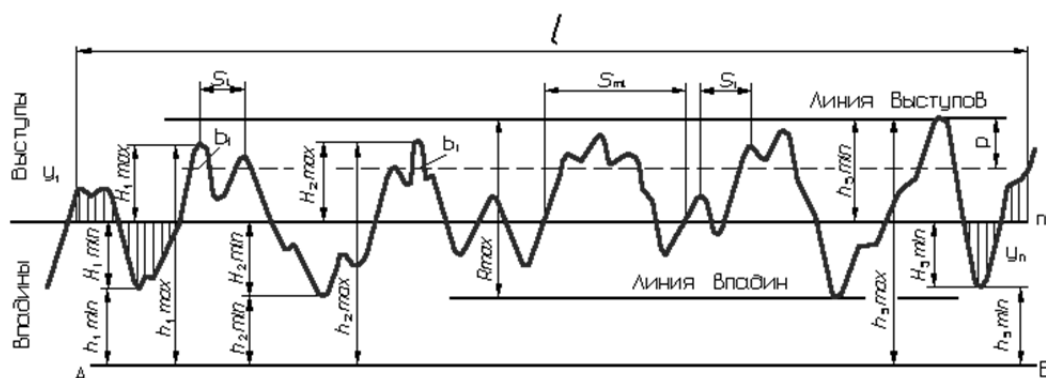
Параметры шероховатости поверхности по ГОСТ 2789-73
